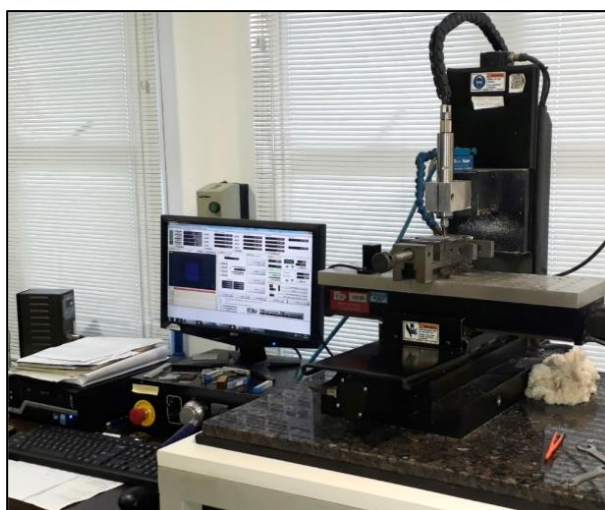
Sistema de microfresamento CNC - Minitch Machinery®
